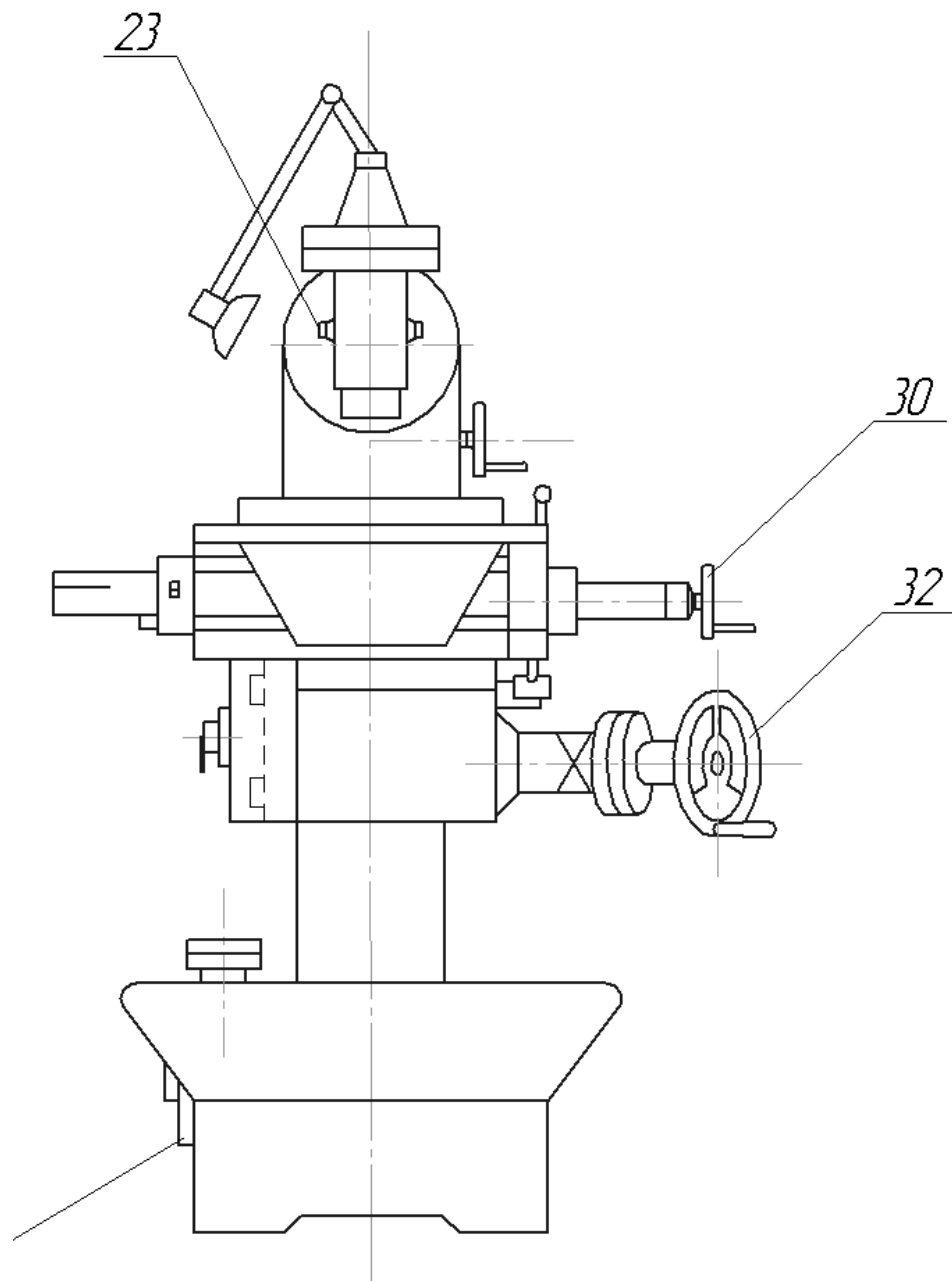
Розміщення органів керування фрезерного верстата
